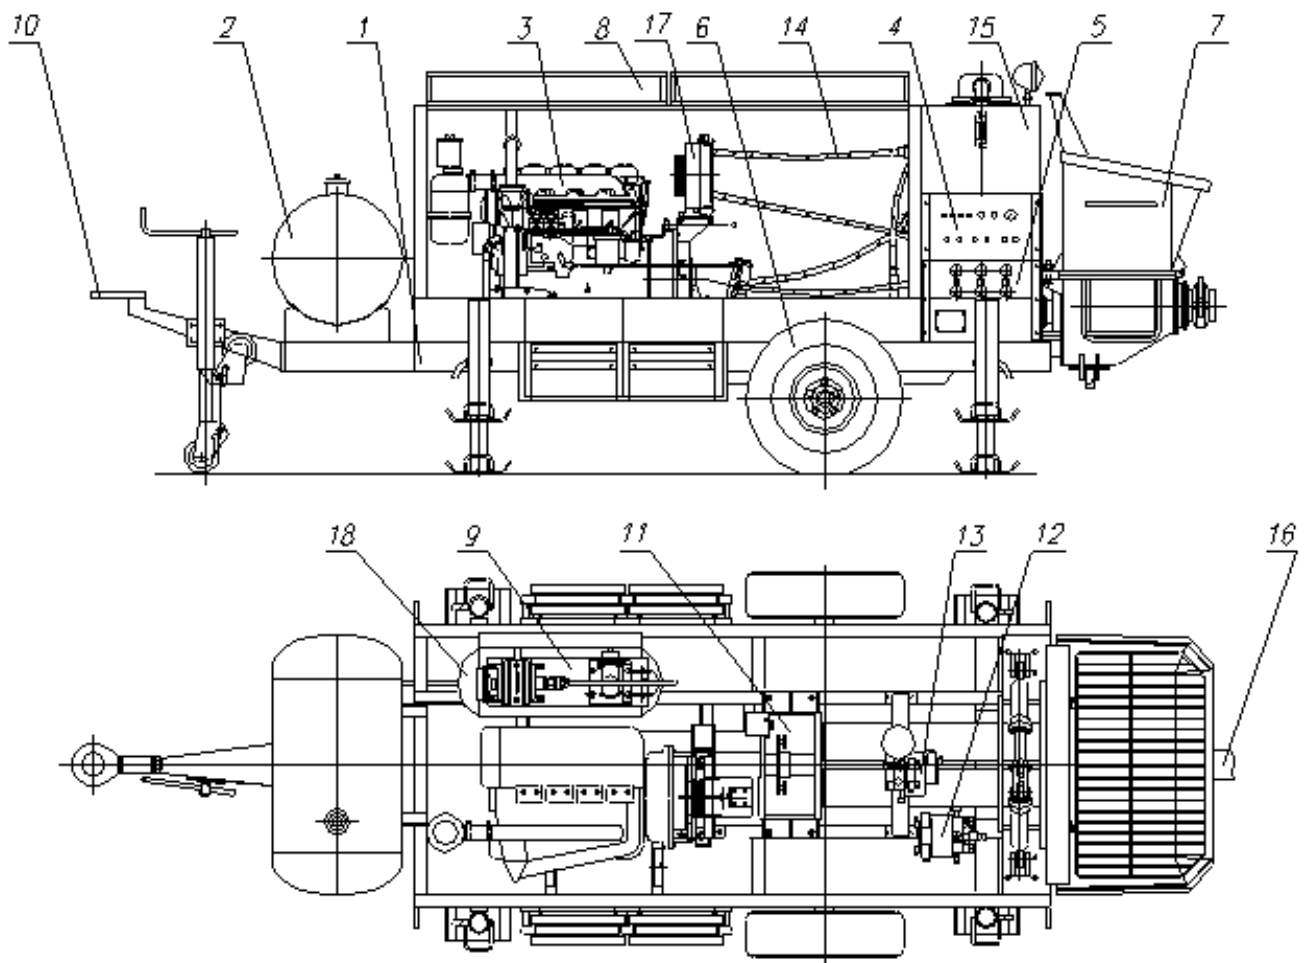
Бетононасос СБ-207А: 1 – рама; 2 – водобак; 3 – привод гидронасосов; 4 – пульт управления; 5 – панель контроля; 6 – установка колес; 7 – воронка приемная; 8 – кожух; 9 – установка компрессора; 10 – дышло; 11 – цилиндропоршневая группа; 12 – блок управления 1; 13 – блок управления 2; 14 – гидросистема; 15 – гидробак; 16 – комплект бетонопроводов; 17 – маслоохладитель; 18 – топливный бак.
